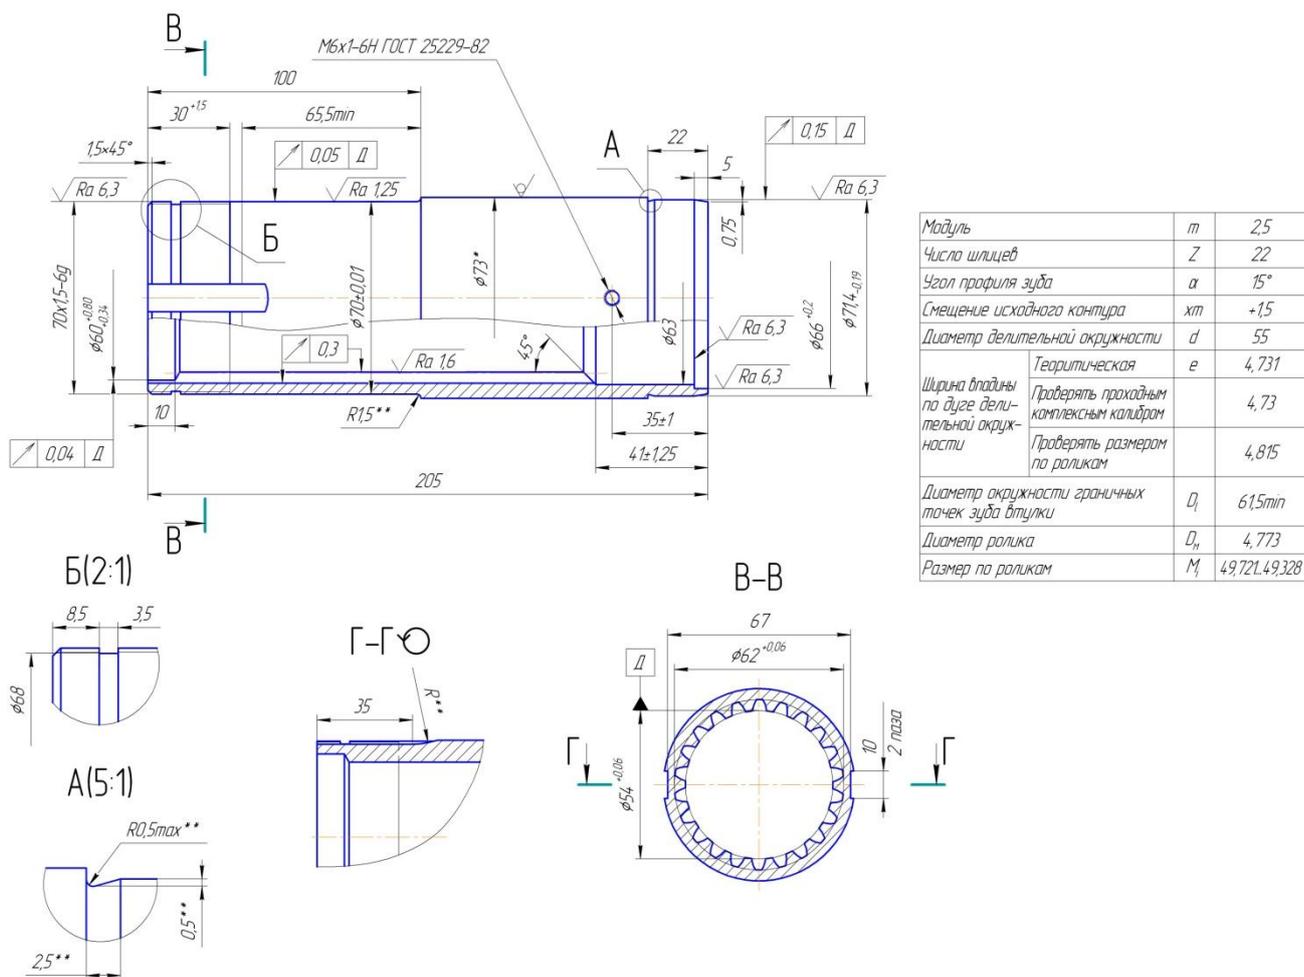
Эскиз детали «Втулка шлицевая»
